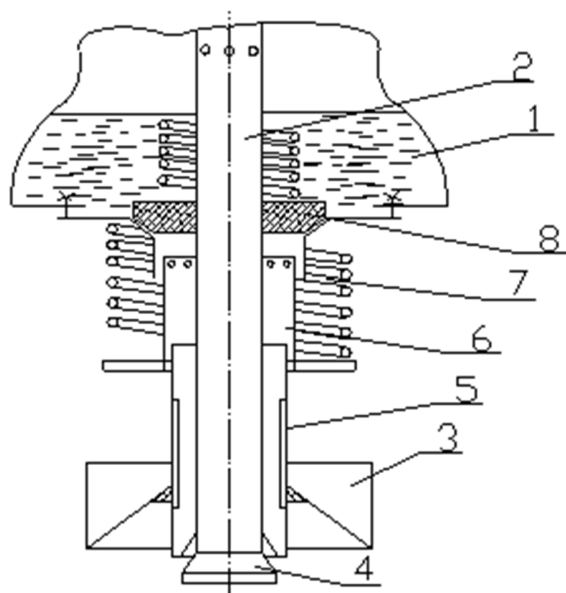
Схема барометричного дозатора за рівнем: 1 – резервуар; 2 – повітряна трубка; 3 – дзвіночок; 4 – зливний клапан; 5 – зливна трубка; 6 – трубка підводу повітря; 7 – пружина; 8 – верхній клапан.
